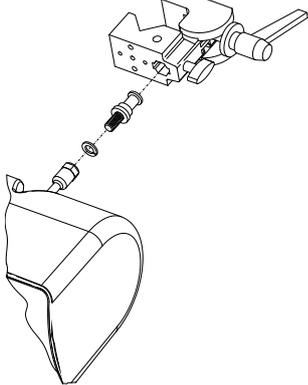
Montage der E6532 Super Clamp zusammen mit E6533 M10 Adapter für Super Clamp
